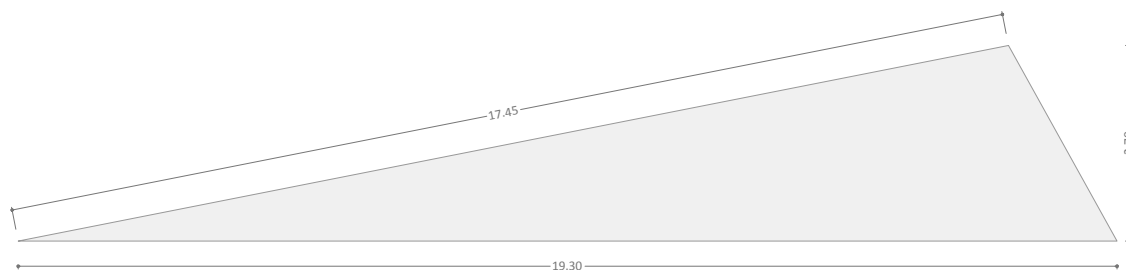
DIMENSIONES LÁMINA TRIANGULAR
